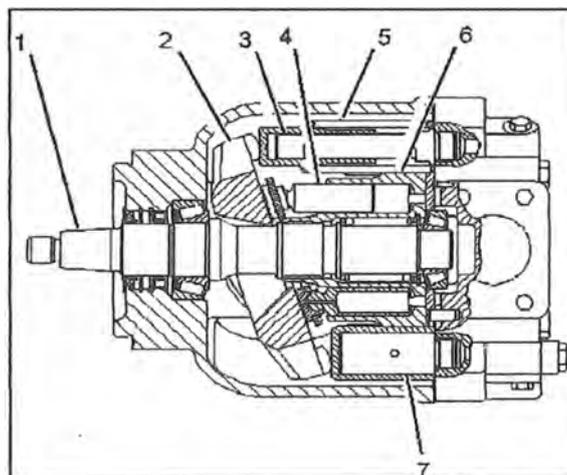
Partes de una Bomba de Pistones Axiales
